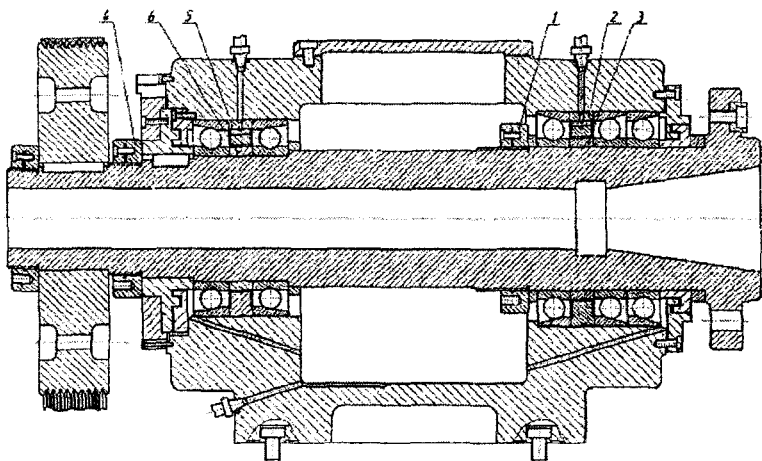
Шпиндельный узел с комплектом шариковых радиально-упорных подшипников типа 36000 со схемой триплекс тандем О-образный в передней опоре и дуплекс О-образный – в задней
